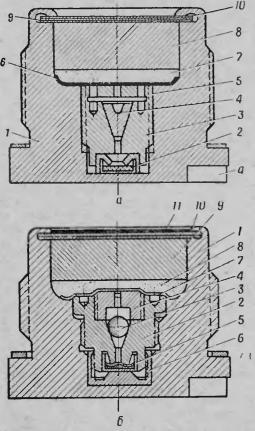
Капсюльные втулки КВ-13У и КВ-13: a — капсюльная втулка КВ-13У; I — корпус: 2 — втулючный капсюль-воспламенитель № 1: 3 — втулка КВ-44 — конус; 5 — гайка: 6 — кружки: a — гнездо для ключа; 6 — капсюльная втулка КВ-13: I — корпус; 2 — наковаленка: 3 — обтюрирующий шарик; 4 — втулка: 5 — капсюль-воспламенитель: 6 — обтюратор; 7 — прокладка из просслитренной бумаги: 8 — пороховая подсыпка; 9 — пороховая петарда: 10 — обтюрирующее кольцо; 11 — латунный кружок
